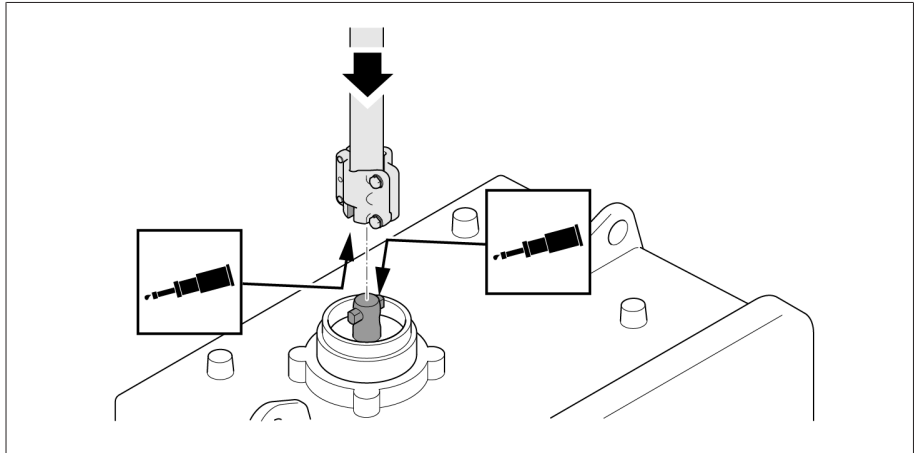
Glisser le tube carré avec la pièce d'accouplement sur l'extrémité d'arbre
